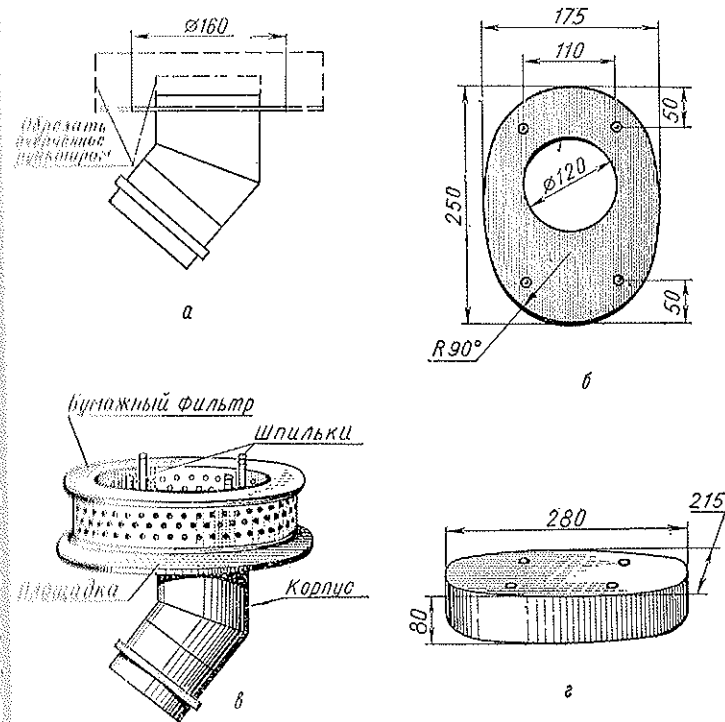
Воздушный фильтр с бумажным элементом: а — обрешетка корпуса; б — площадка — основание элемента; в — крышки; г — фильтр в сборе.
